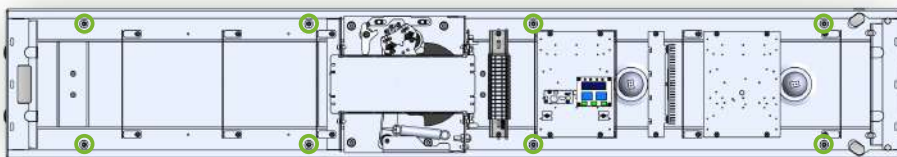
Места соединения винтами основания крышки корпуса механизма (вид сверху)
